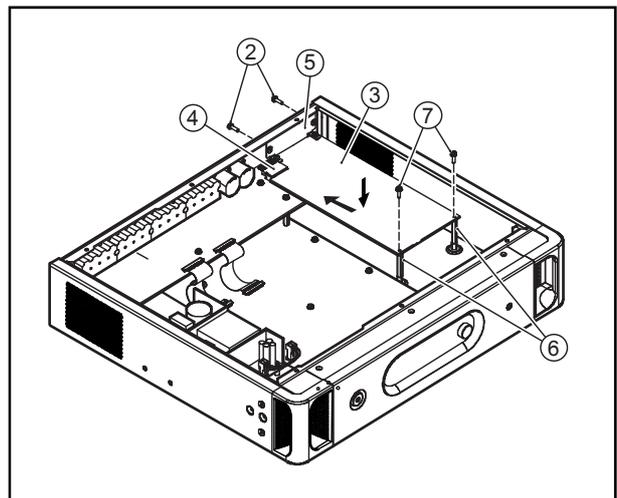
Установка интерфейсного модуля в корпус передатчика
